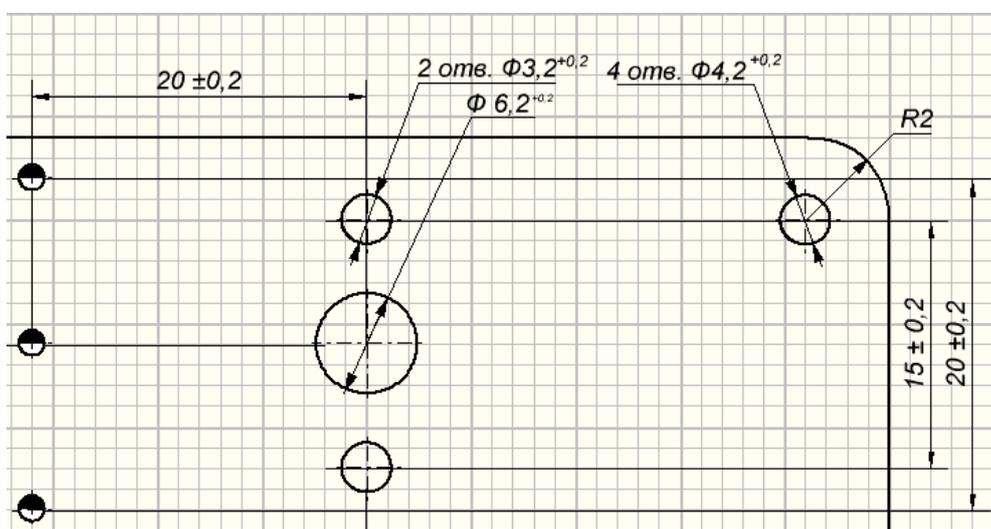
Установочные размеры отверстий для переменного конденсатора
